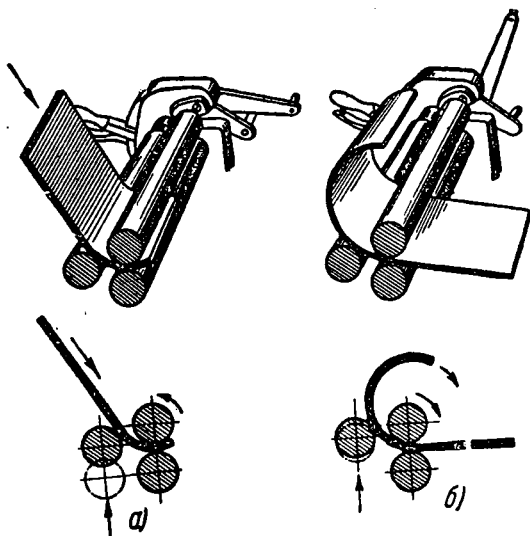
Гибка заготовки на листогибочном трехвалковом станке:
